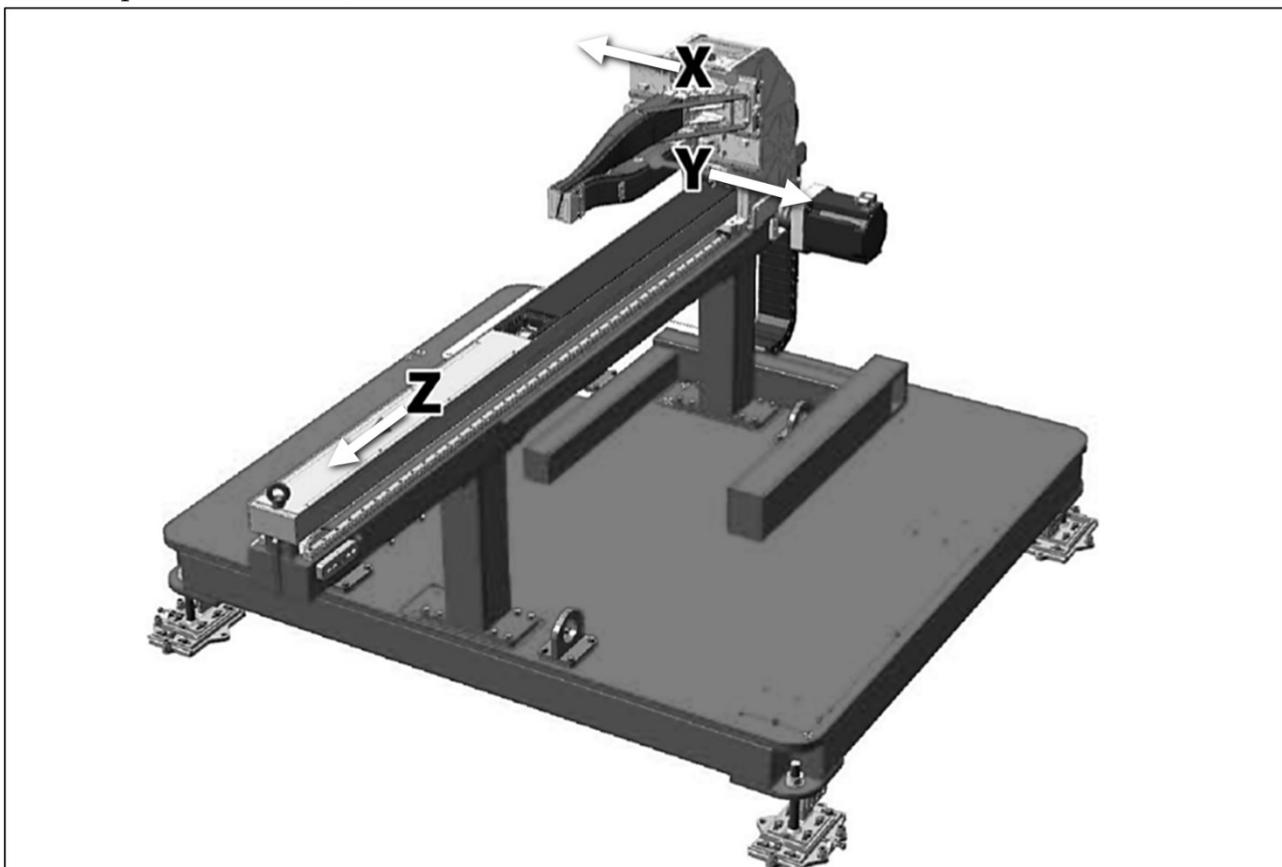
Rappresentazione tridimensionale della struttura della macchina di asservimento alla pressa ad iniezione
